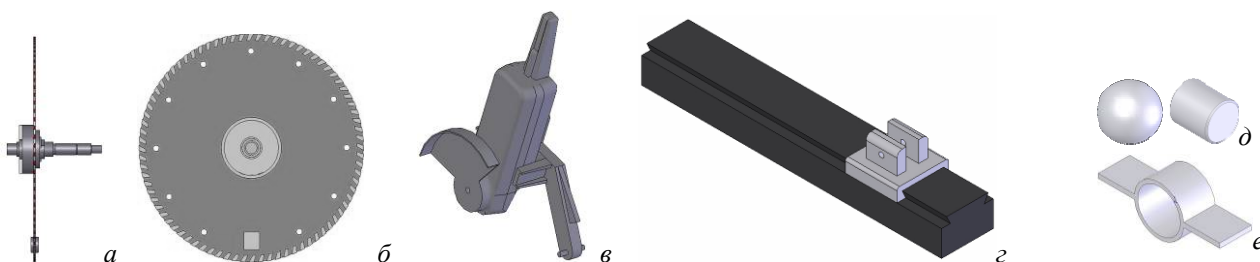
Елементи моделі: а – корпус АБ, диск з додатковим дисбалансом, насаджені на вал, вид збоку, б – вид спереду; в – корпус РШМ на кулісі; г – станина; д – куля, ролик; е – рухома перегородка
